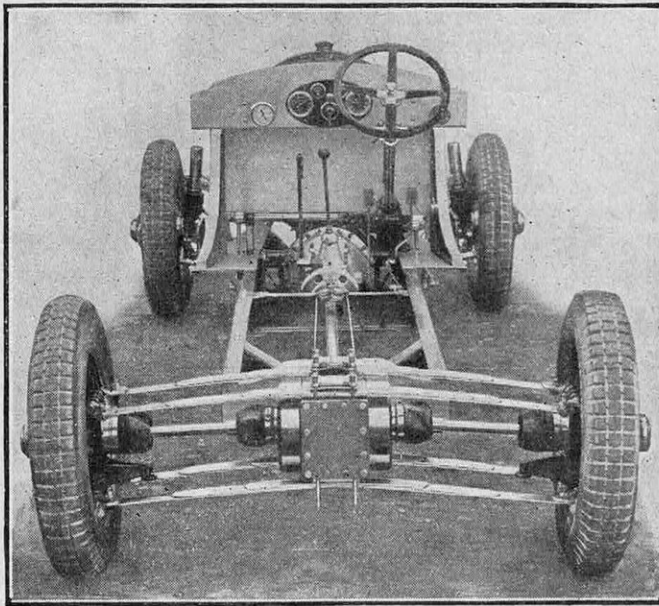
VUE ARRIÈRE D'UN CHASSIS NON CARROSSÉ D'UNE VOITURE A ROUES INDÉPENDANTES
